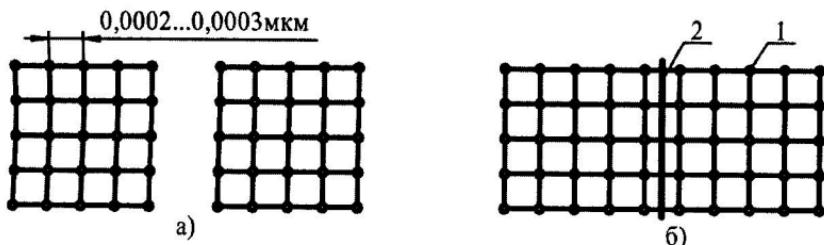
Схема утворення зварного з'єднання між двома монокристалами: а) – монокристали до зварювання; б) – монокристали після зварювання; 1 – іон кристалічної гратки; 2 – границя зварного з'єднання
